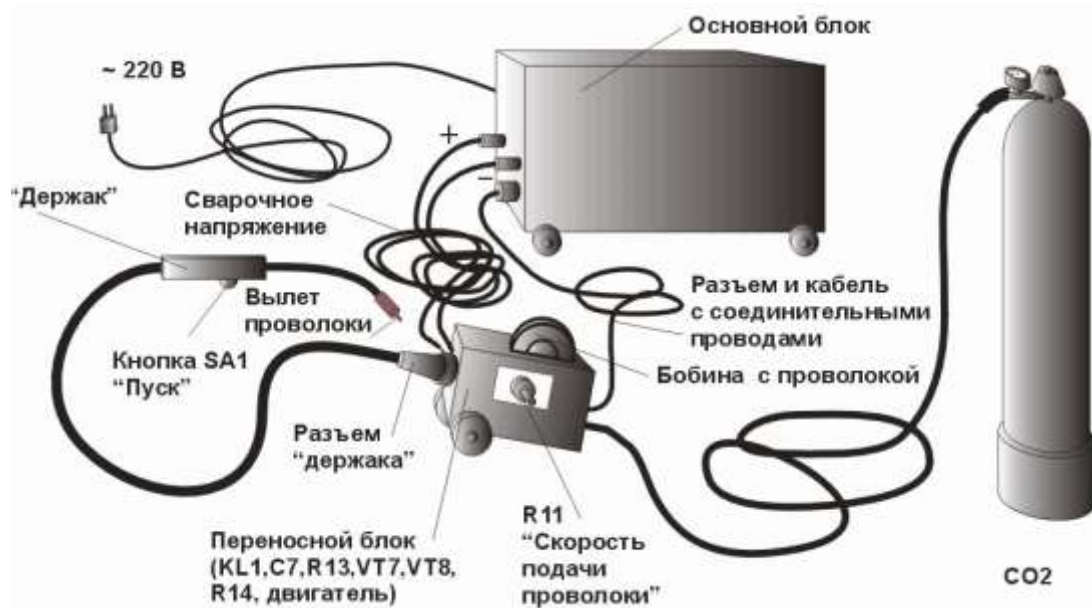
Загальний вигляд зварювального напівавтомата
